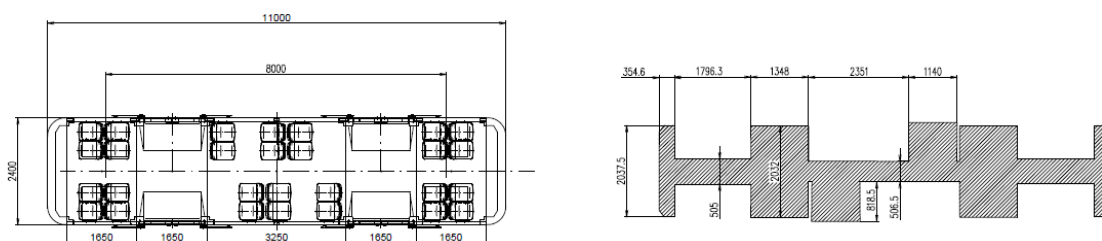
Půdorys uspořádání - varianta 3. [autor DP]
